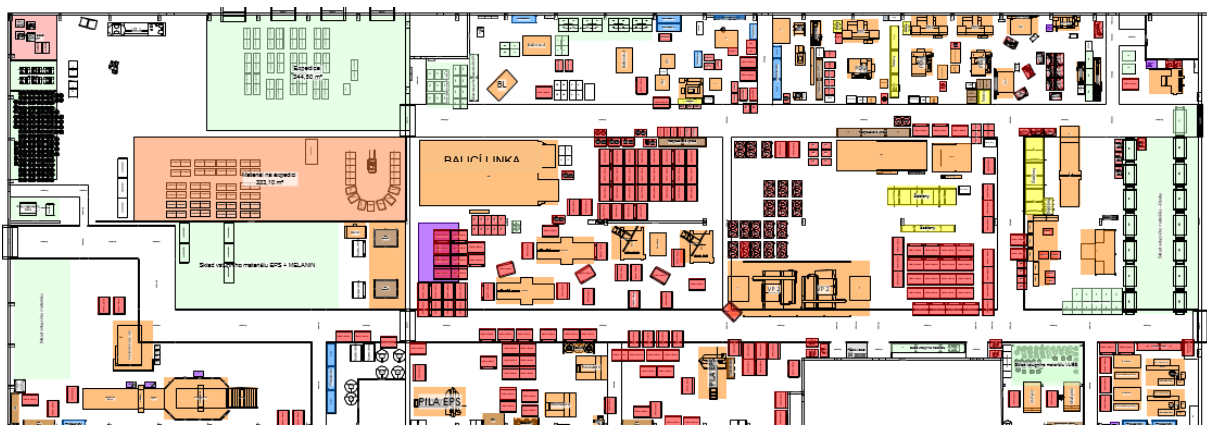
Půdorys haly s dopravními cestami. [Zdroj vlastní]
